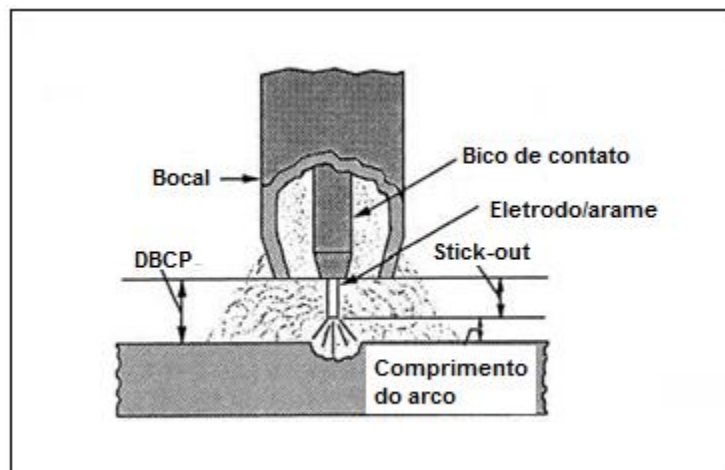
Esquema construtivo do bocal da tocha de soldagem e características [Adaptado de Fortes, 2005].
